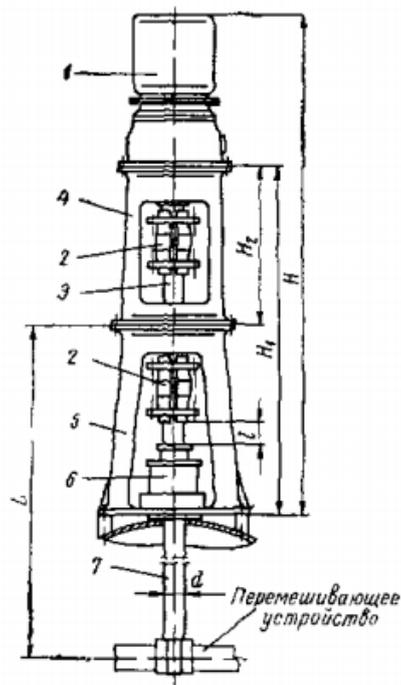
Привод вертикальный с одной промежуточной опорой вала.
